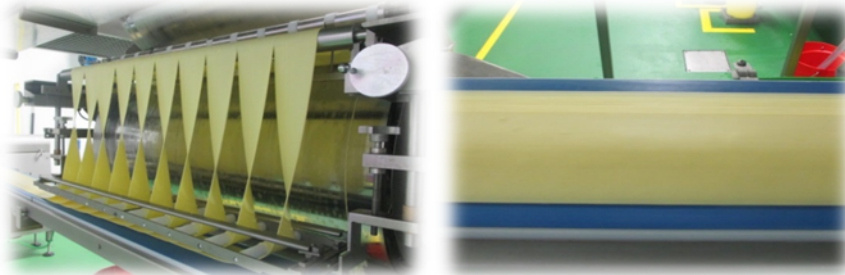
Corte en tiras longitudinales y apilamiento.
